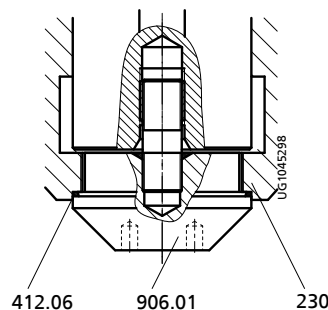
Крепление рабочего колеса М100х2 (для проточной части К 350-710)
